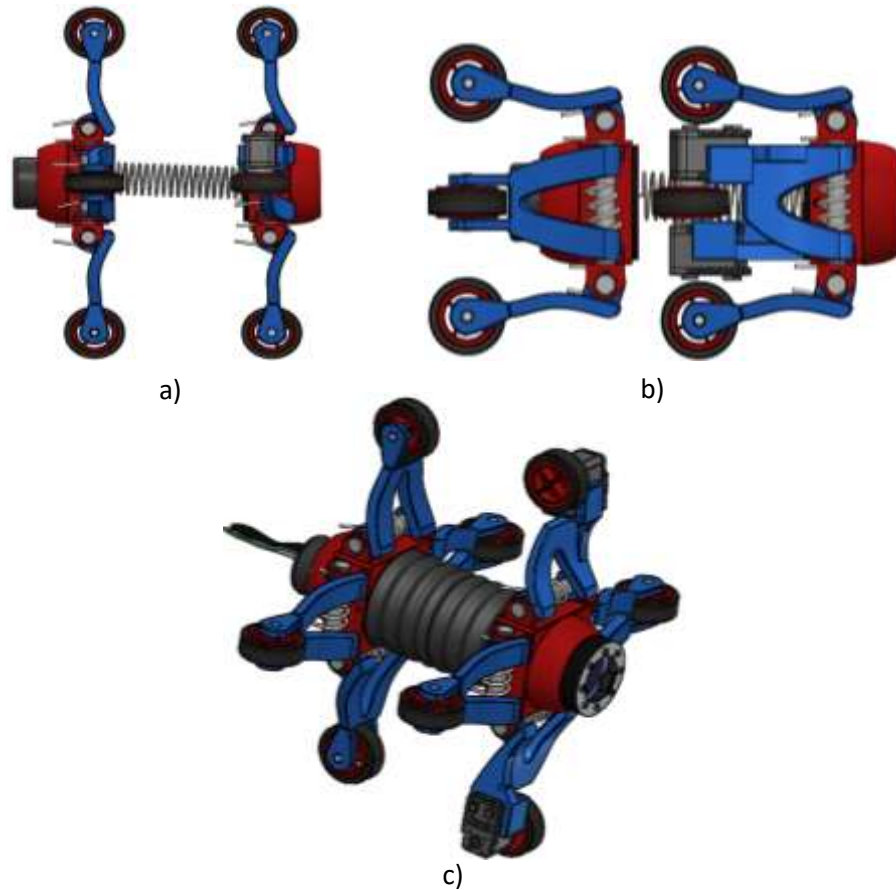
Diseño CAD del mecanismo adaptable para robot de inspección de tuberías. a) Vista lateral con extremidades extendidas b) Vista lateral con extremidades retraídas c) Vista isométrica con extremidades extendidas
